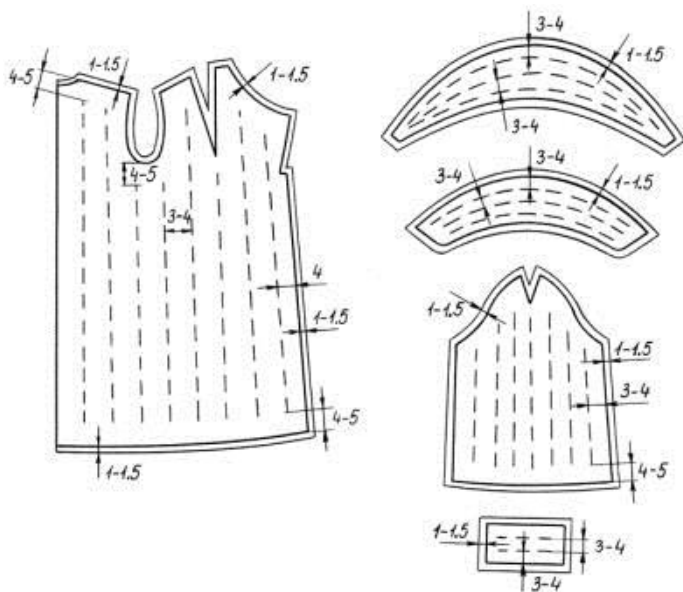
Ручний спосіб з'єднання бавовняної прокладки з деталями хутряного верху
